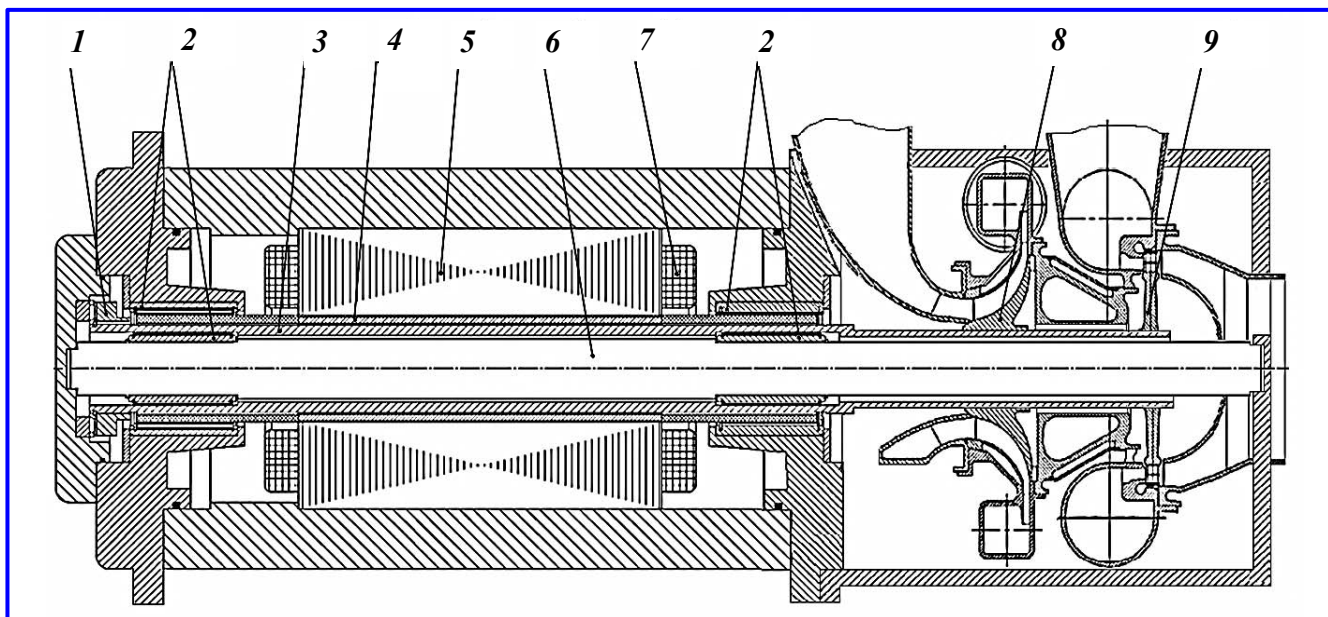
Эскиз компоновки турбокомпрессорной системы: 1 – упорный подшипник; 2 – опорный подшипник; 3 – внутренний ротор; 4 – внешний ротор; 5 – сердечник статора; 6 – опорный неподвижный вал; 7 – обмотка статора; 8 – колесо компрессора; 9 – колесо турбины
